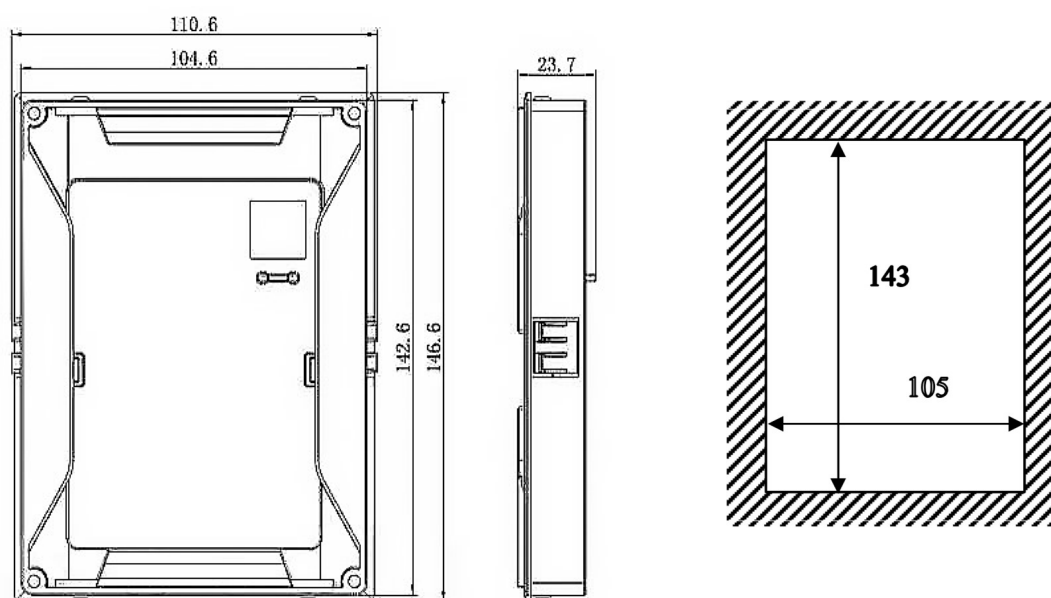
Внешний вид преобразователей E5-9600-600H...900H, E5-9600-600K...900K
